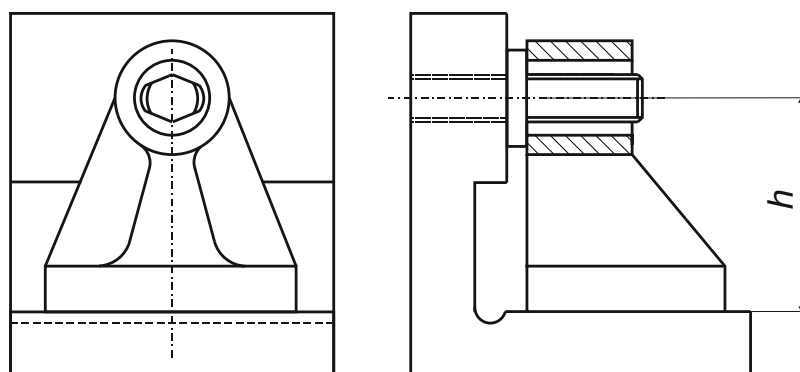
Установка детали по плоской и цилиндрической поверхности
